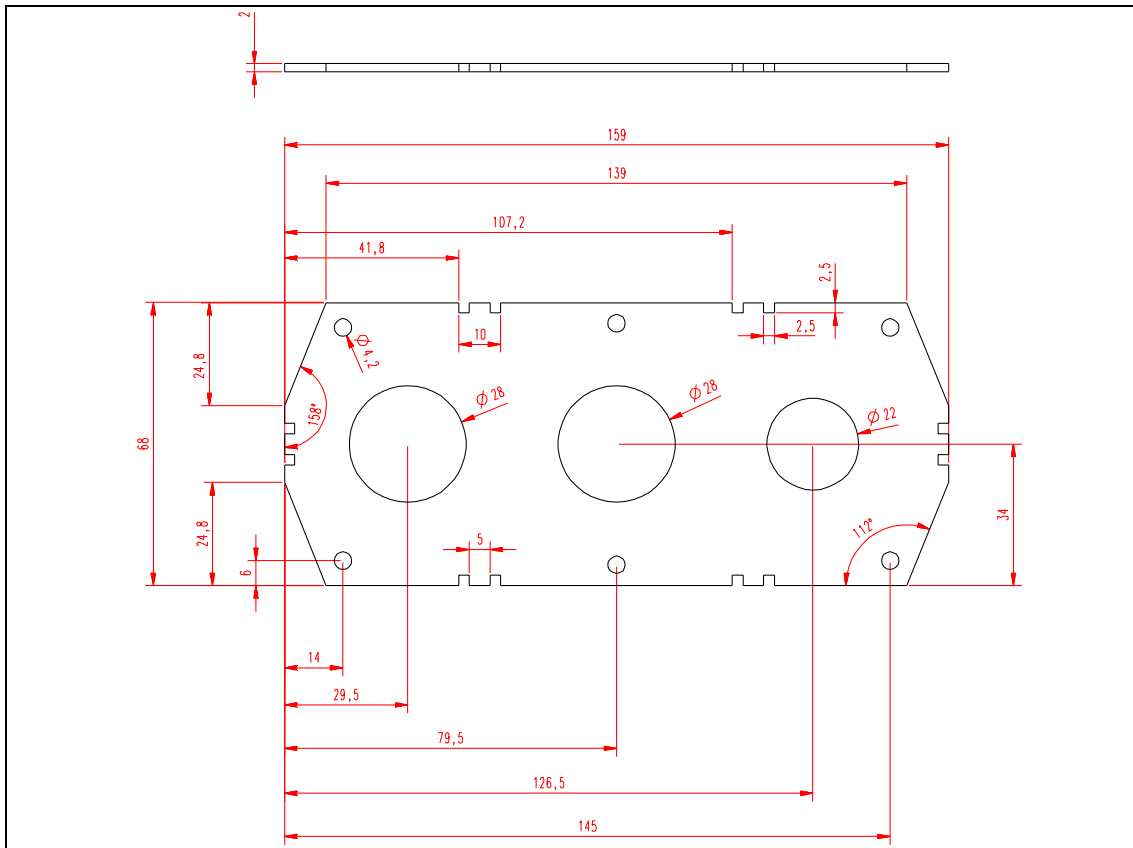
Plaque d'entrée des câbles, installation UL MM5
